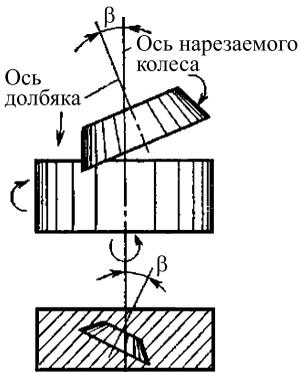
Схема зуботочения цилиндрических зубчатых колес
